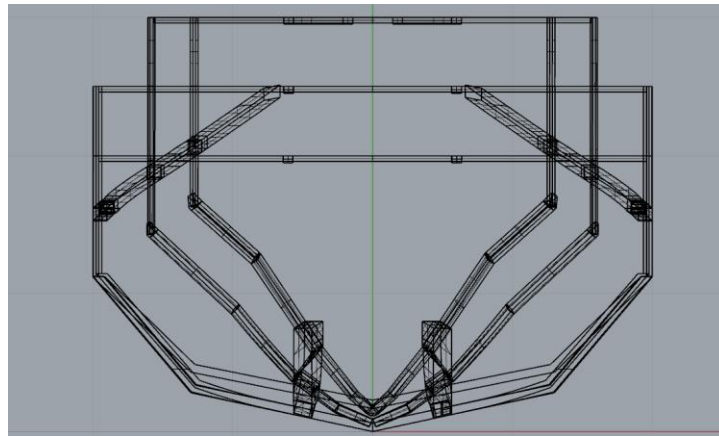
Disposición general de los refuerzos. Vista caja de cuadernas
